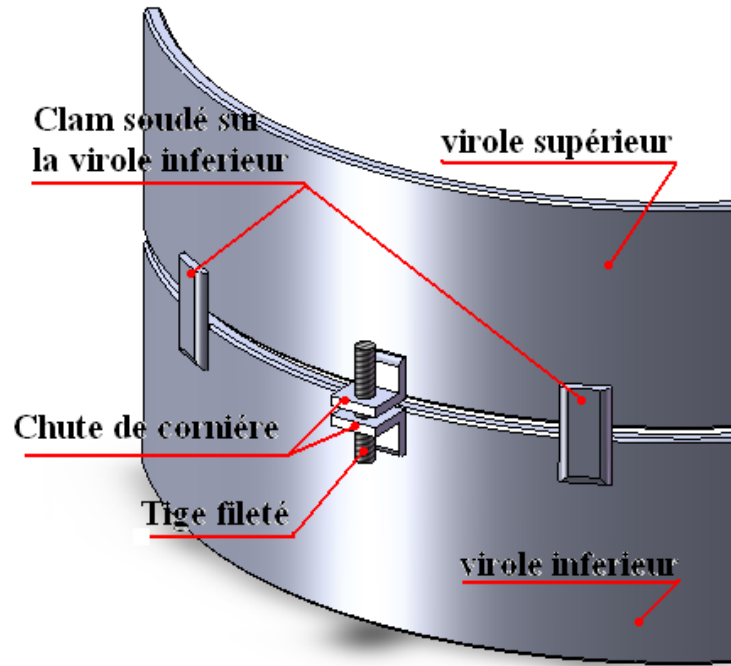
Assemblage des viroles (soudage des joints horizontaux)
